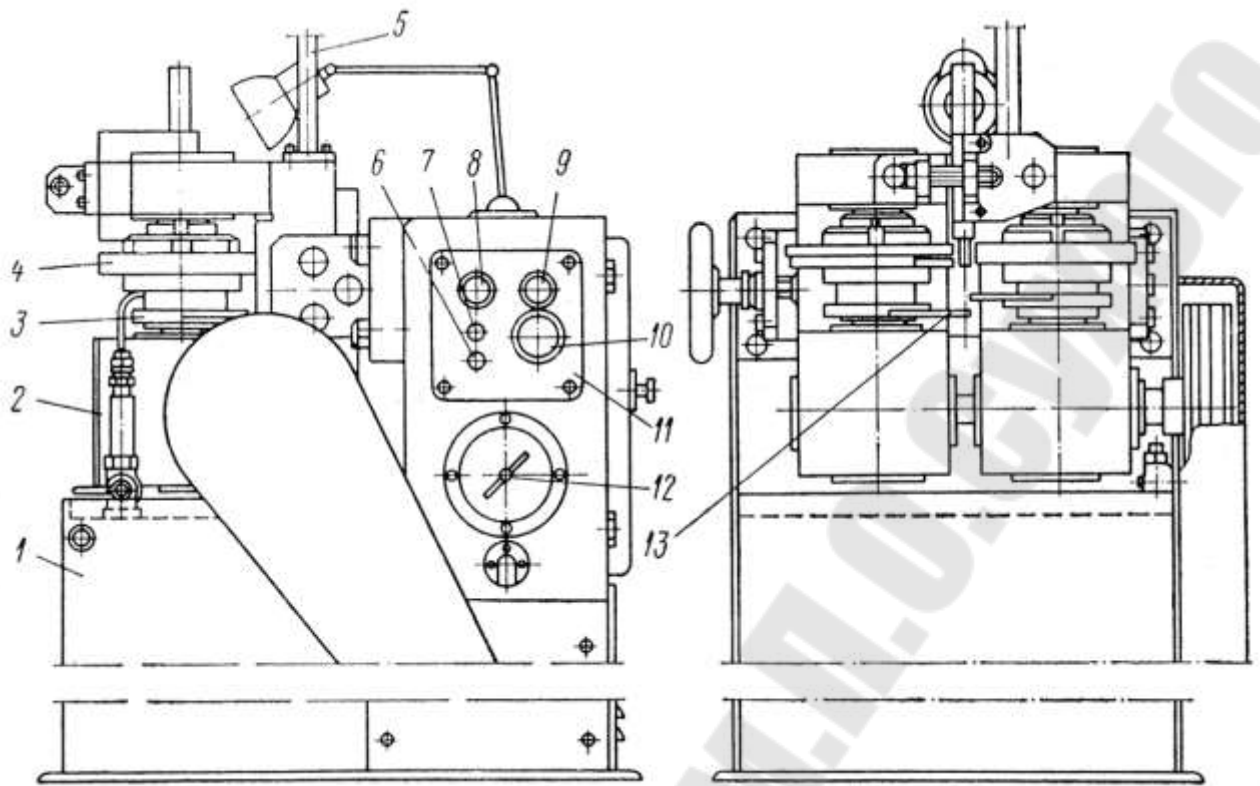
Эскиз общего вида специального отрезного автомата модели СИ-052: 1 – станина; 2 – клеть; 3 – надламывающий кулачок; 4 – рабочие диски; 5 – направляющая для прутка; 6 – переключатель освещения; 7 – переключатель охлаждения; 8 – кнопка «Пуск»; 9 – кнопка «Стоп»; 10 – лампочка «Напряжение»; 11 – пульт управления; 12 – вводный выключатель; 13 – упор прутка
